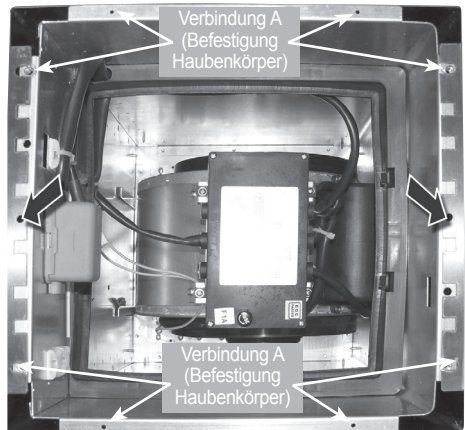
(Abb. ähnlich): Hier (schwarze Pfeile) werden die beiden Schrauben (10) an der Unterseite des Motorblocks (12) eingesetzt, um die Blechhaken (14) zu befestigen, die später den Grundschaft (3) halten.
